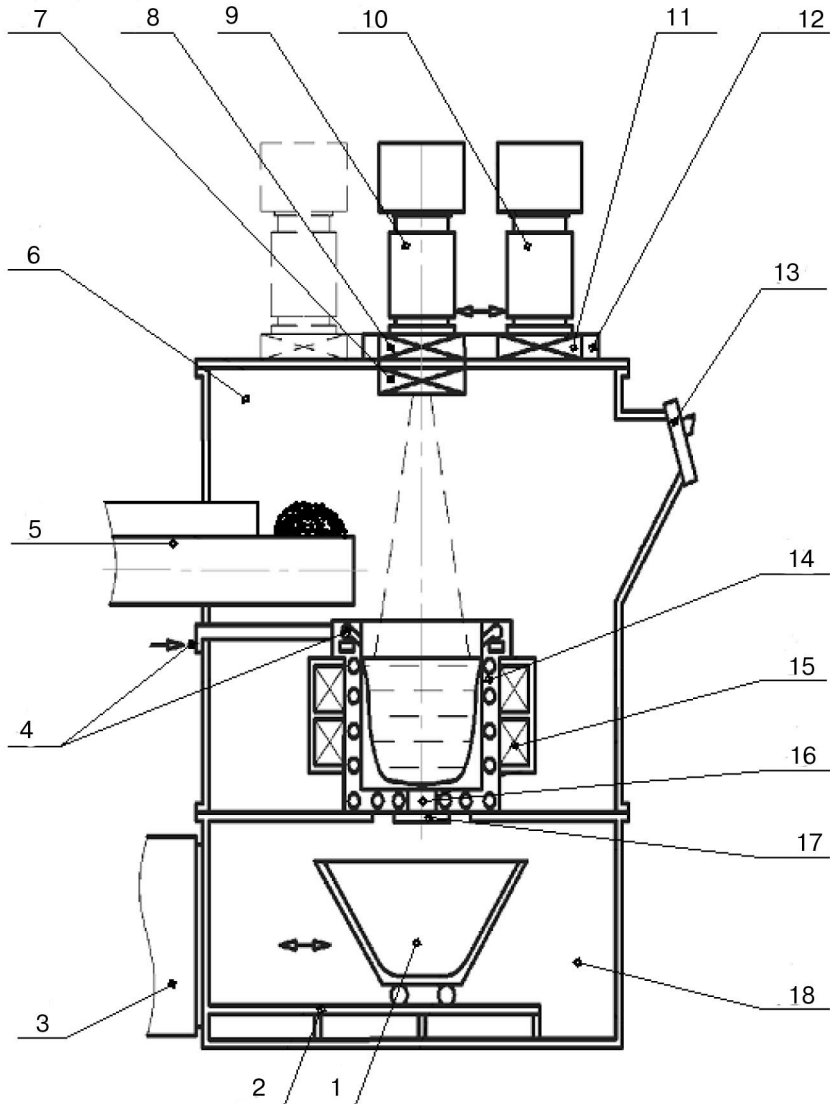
Схема электронно-лучевой литейной установки со сменными нагревателями: 1 – литейная форма; 2 – эстакада; 3 – шлюзовая камера; 4 – устройство подачи рафинирующего газа; 5 – устройство подачи шихты на переплав; 6 – плавильная камера; 7 – пушечный затвор плавильной камеры; 8 – затвор средневacuумной пушки; 9 – средневacuумная пушка ВТР; 10 – низковacuумная пушка ВТР; 11 – затвор низковacuумной пушки; 12 – передвижная плита пушек; 13 – смотровая система; 14 – тигель; 15 – система ЭМП тигля; 16 – сливное отверстие; 17 – крышка сливного отверстия; 18 – камера литейных форм
